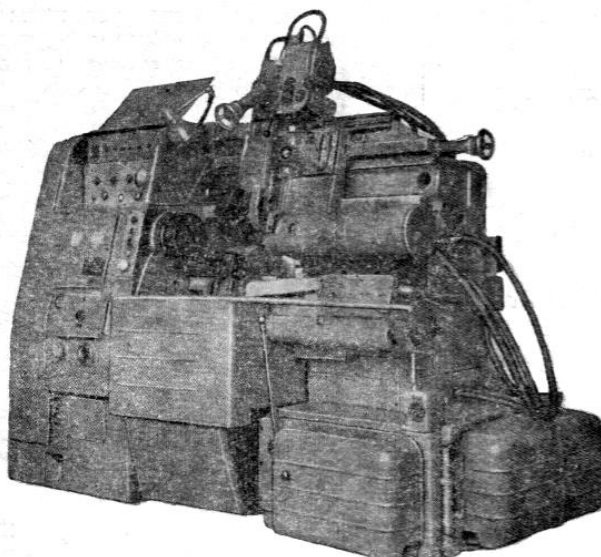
Токарний багаторіздевий напівавтомат модель 1712
